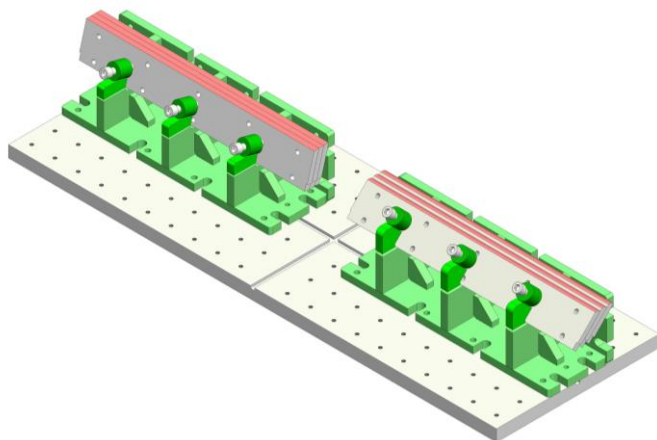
Приспособлението с установени детайли ножове за грайферна кофа КМ622 – 1000 mm.
